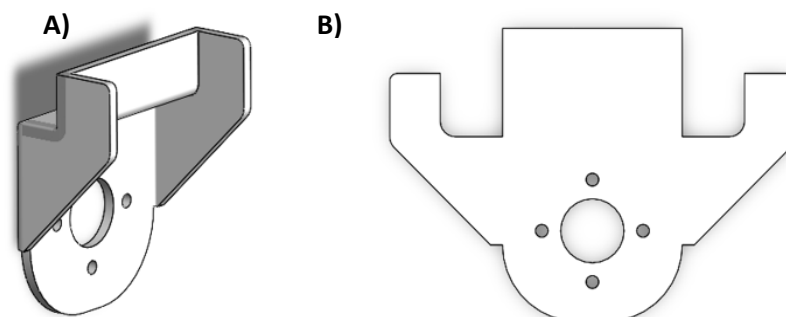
A) Suport del motor superior; B) Desplegament del suport del motor superior.
